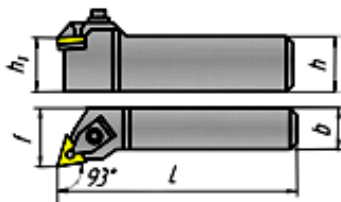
Габаритные геометрические размеры резца с механическим креплением сменной твердосплавной режущей пластины
